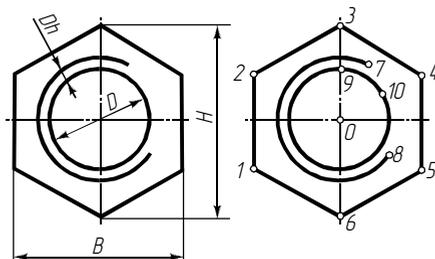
Исходный чертеж и чертеж с указанными опорными точками
